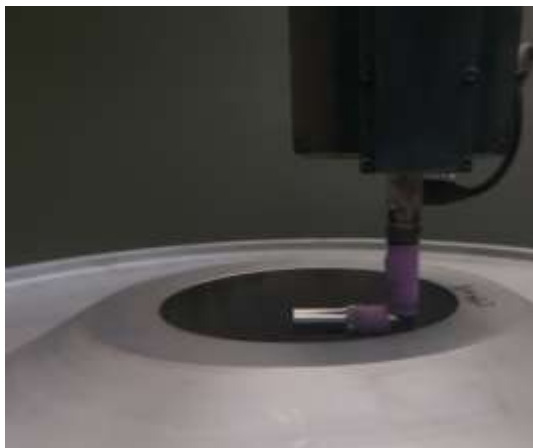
Контроль заготовки диска фокусированным иммерсионным преобразователем с поверхности центрального отверстия
